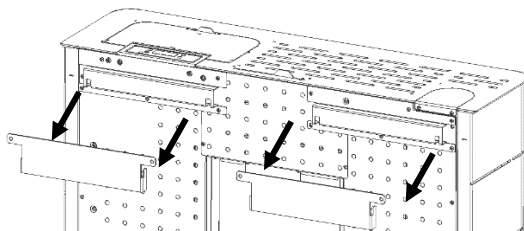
Colocação do equipamento nos apoios fixos na parede
